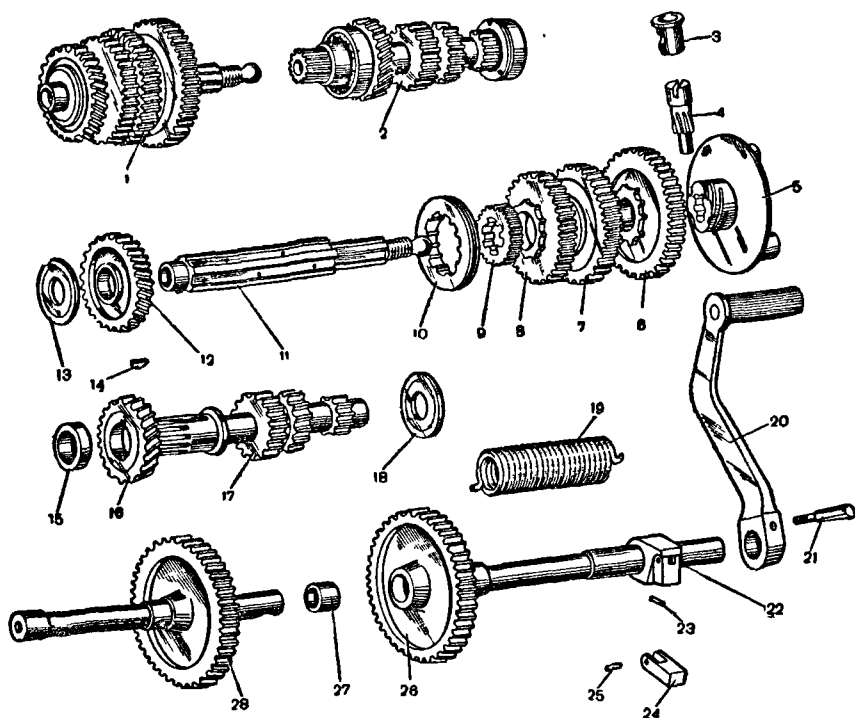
Вали и зубчатые колеса коробки передач мотоциклов «Урал»: 1 — ведомый вал в сборе; 2 — ведущий вал в сборе; 3 — втулка привода спидометра; 4 — зубчатое колесо привода спидометра; 5 — диск муфты карданного вала; 6, 7, 8, 12 — зубчатые колеса первой, второй, третьей и четвертой передач ведомого вала; 9 — муфта ведомого вала; 10 — муфта включения передач; 11 — ведомый вал; 13, 18 — маслоотбойные шайбы; 14 — шпонка; 15 — муфта ведущего вала; 16 — зубчатое колесо четвертой передачи ведущего вала; 17 — ведущий вал; 19 — пружина пускового механизма; 20 — рычаг пускового механизма; 21 — клиновидный болт; 22 — вал пускового механизма; 23, 25 — оси собачки; 24 — собачка; 26 — зубчатое колесо пускового механизма; 27 — втулка вала; 28 — вал пускового механизма с зубчатым колесом
